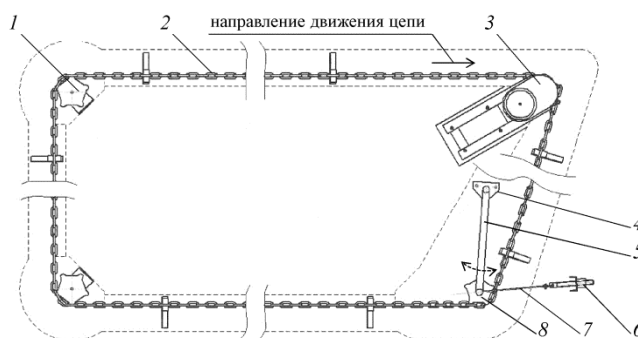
Горизонтальный транспортер с натяжным устройством винтового типа:
